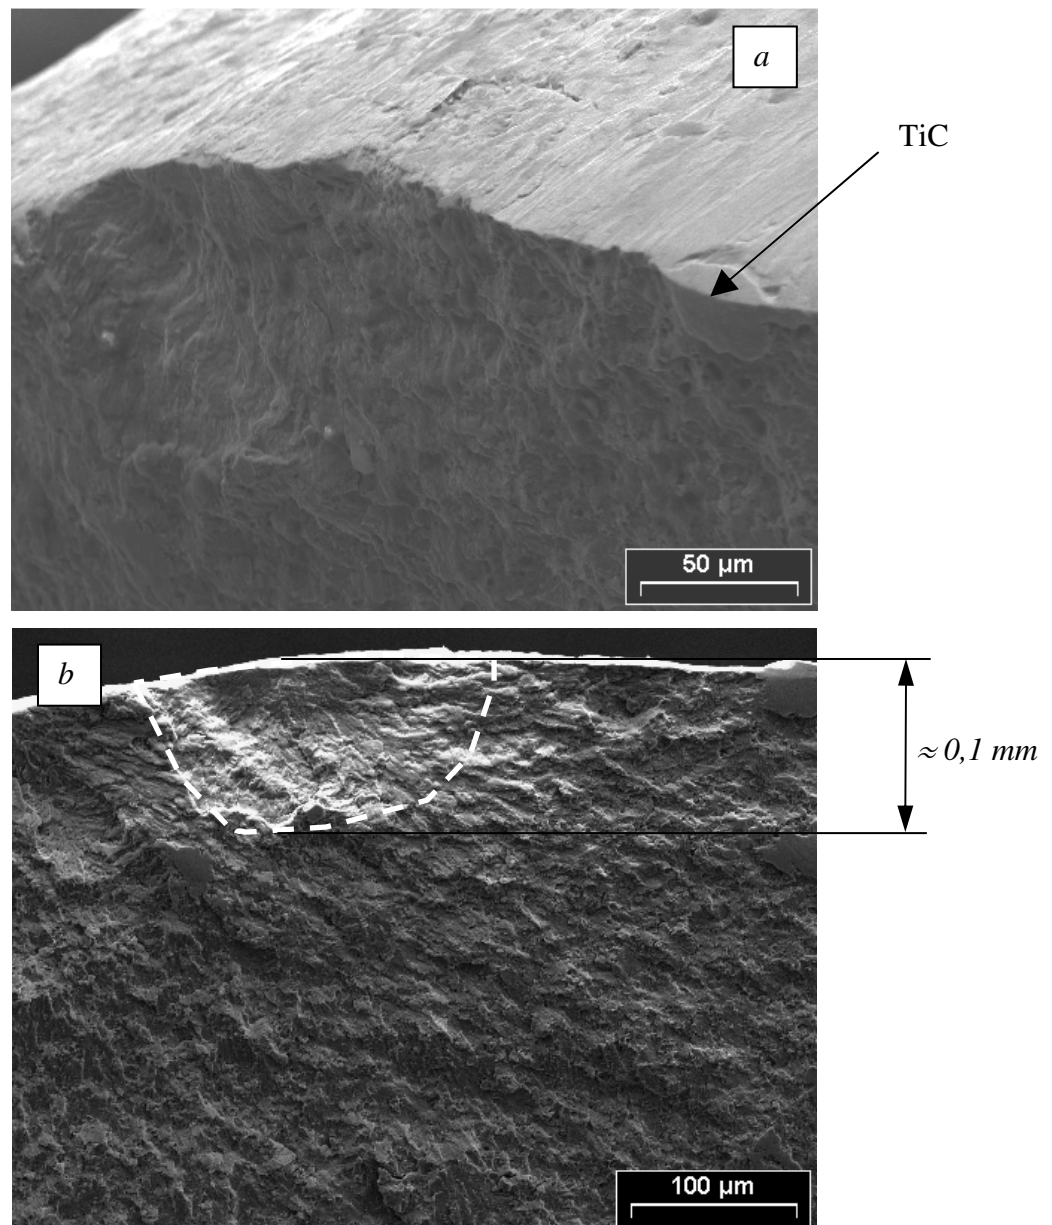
Detalles de la zona de inicio de fisura
